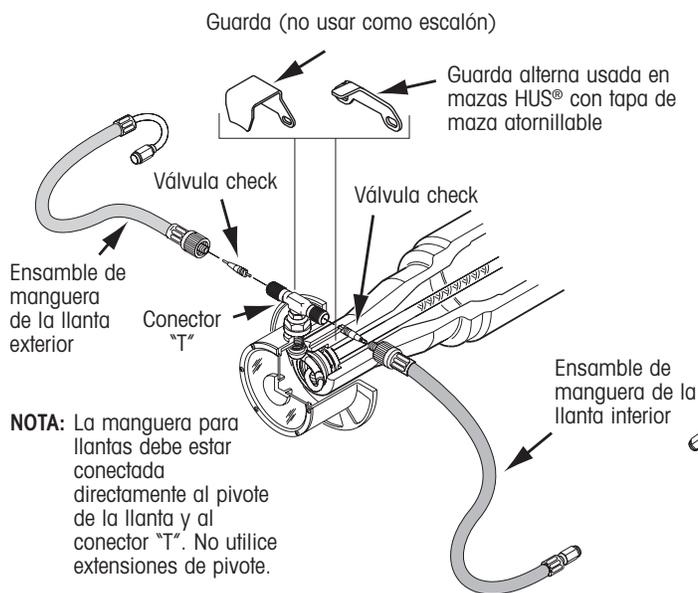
Instale la manguera para llantas en el pivote de la llanta
